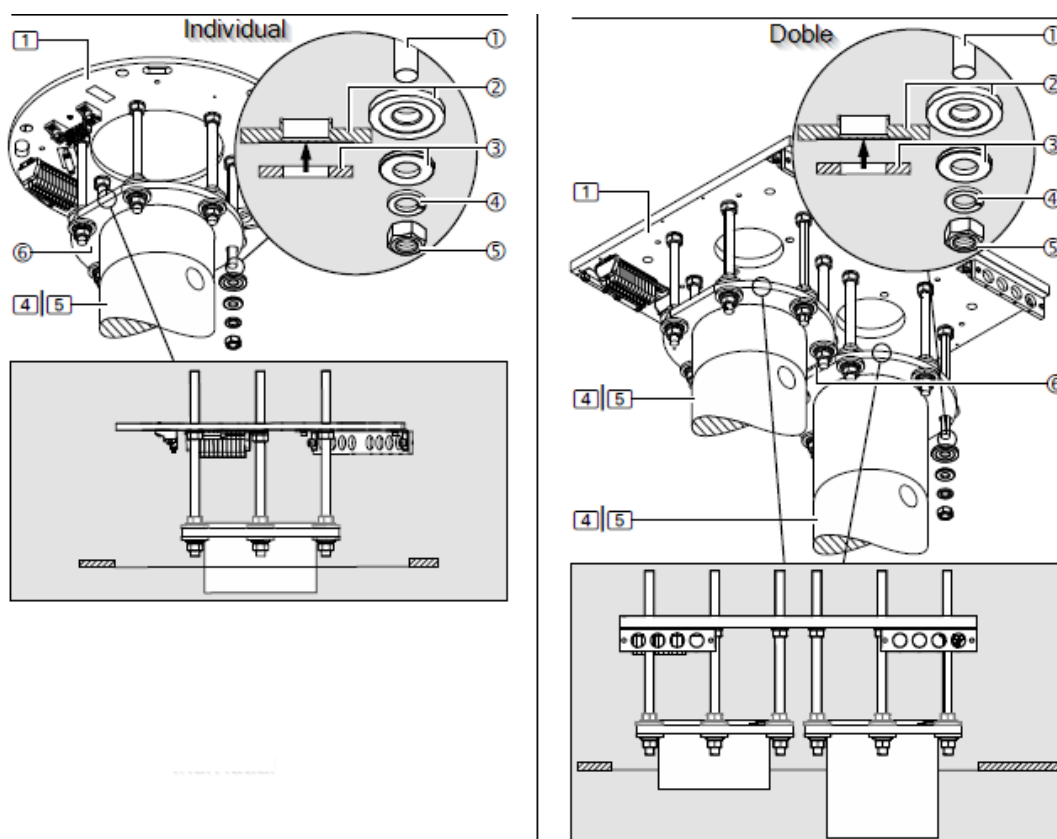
Assemblage de la bride du tube de toit sur les boulons filetés
